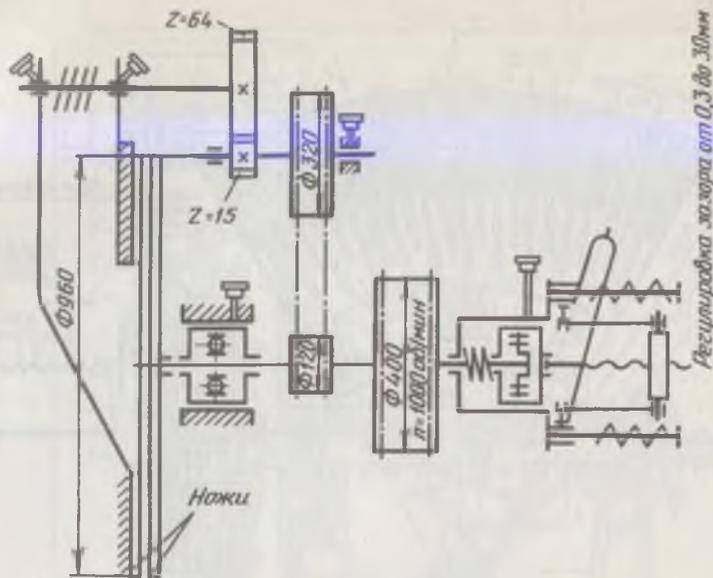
Кинематическая схема дискового шелушителя типа МШВ
